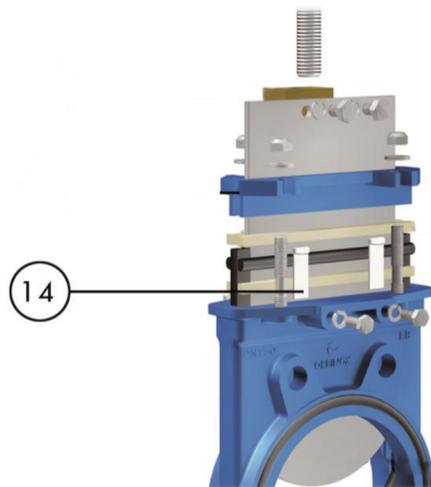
Dibujo detallado del montaje en válvula de compuerta con guías de desgaste (14)
